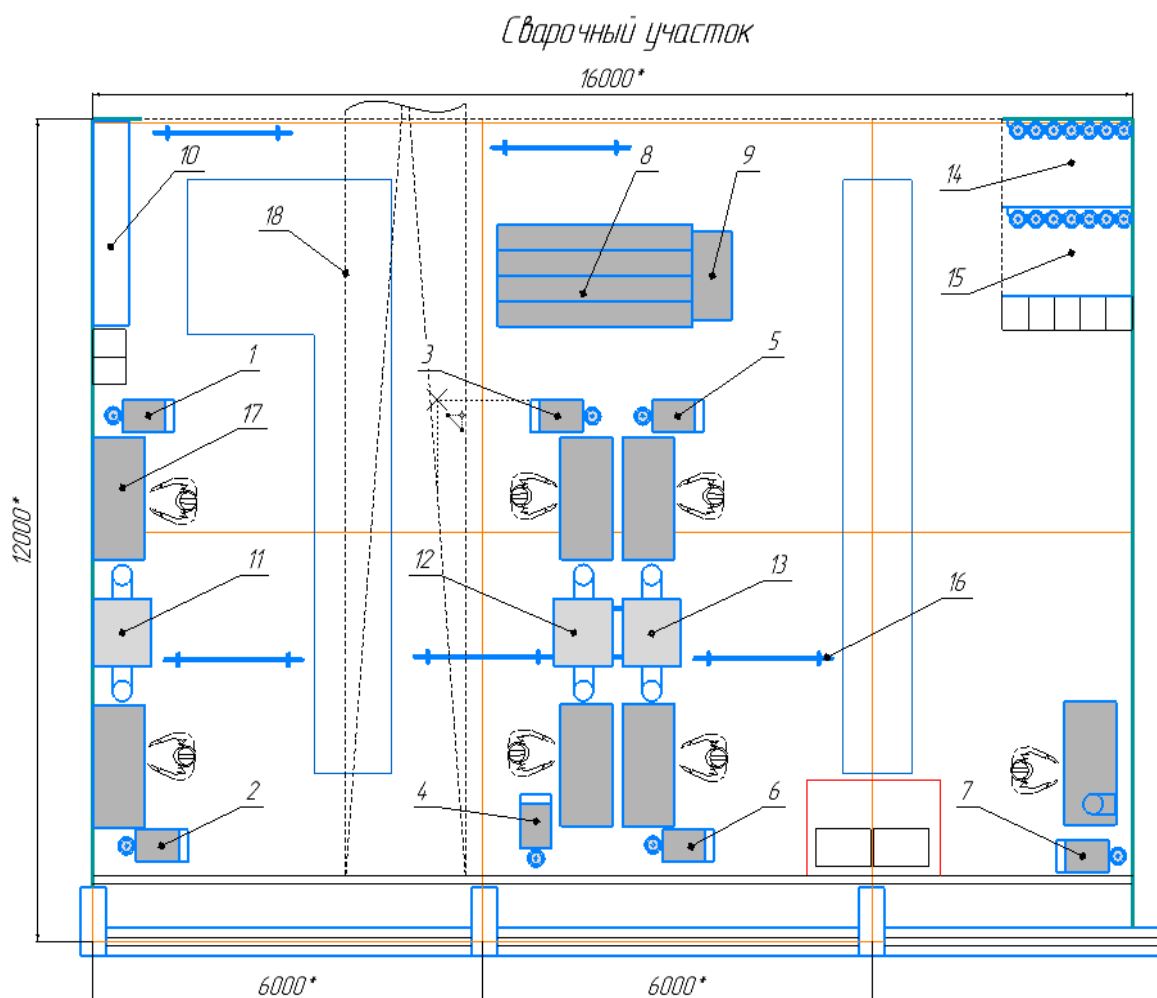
Технологическая схема размещения основного оборудования на участке ручной полуавтоматической сварки
